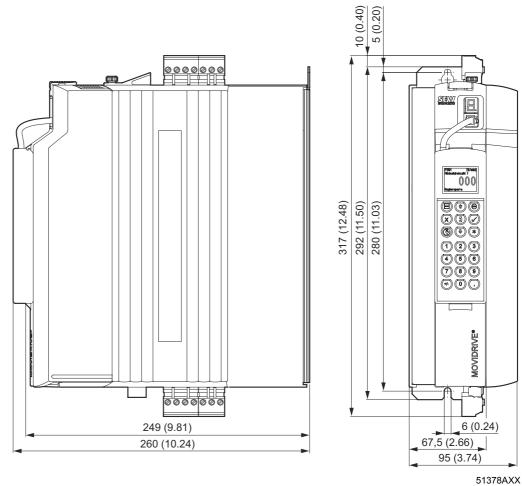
Dimensões MDX61B, tamanho 0M, dimensões em mm (in)
